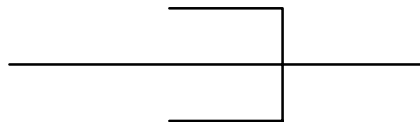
Symbole pour le dessin d'un assemblage à coller
